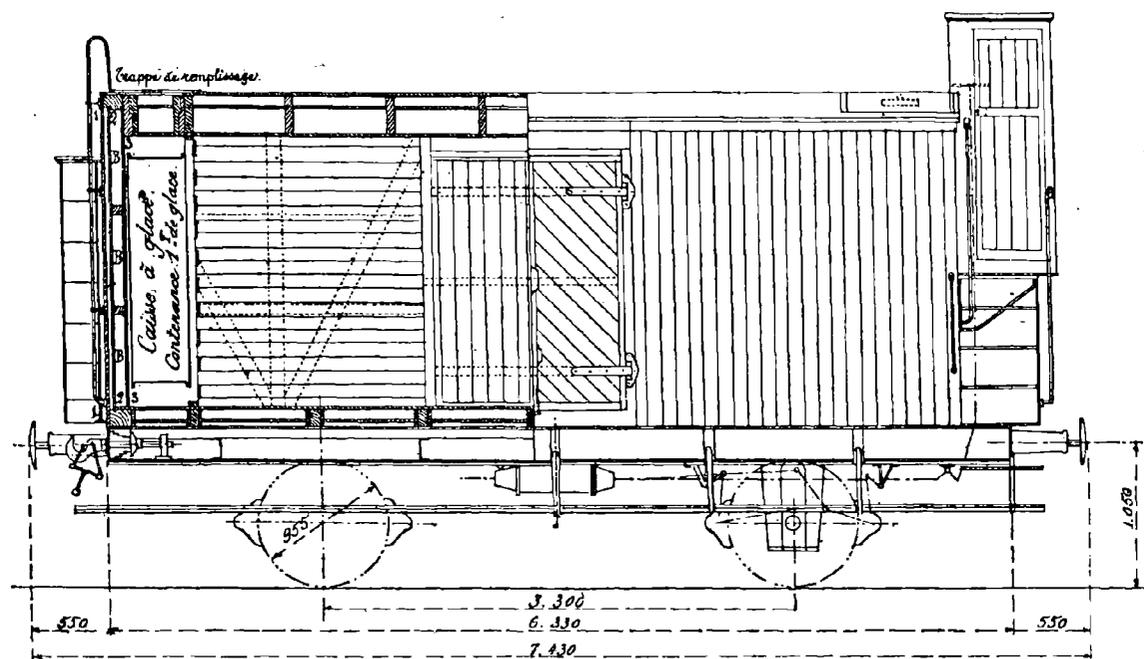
Wagon Hall construit par la Société Dyle et Bacalan; coupe longitudinale.
